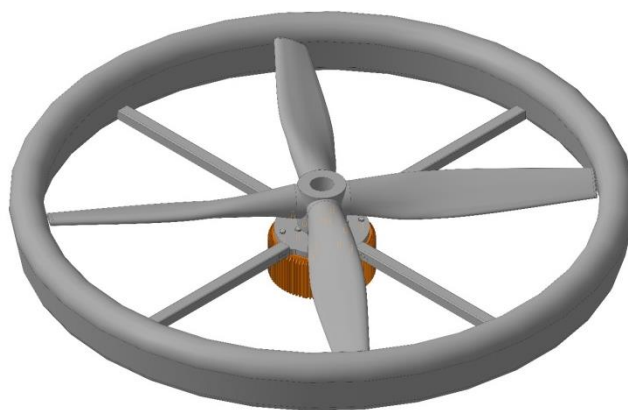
Модель сборки цельноповоротного винта (без узла навески)
